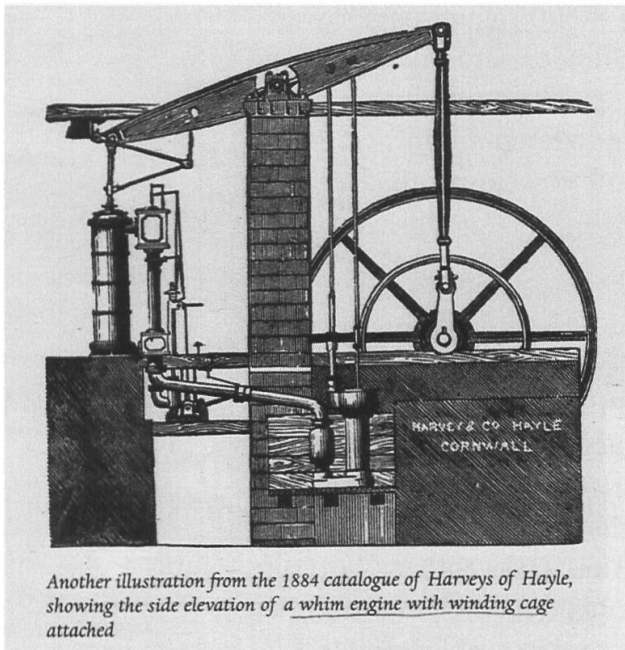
(links) Balancier-Dampfmaschine mit Zylinder, Kolbengestänge, Balancier-Arm, Pleuelgestänge und Schwungrad für eine Förderanlage (whim) (Mark 2007).
